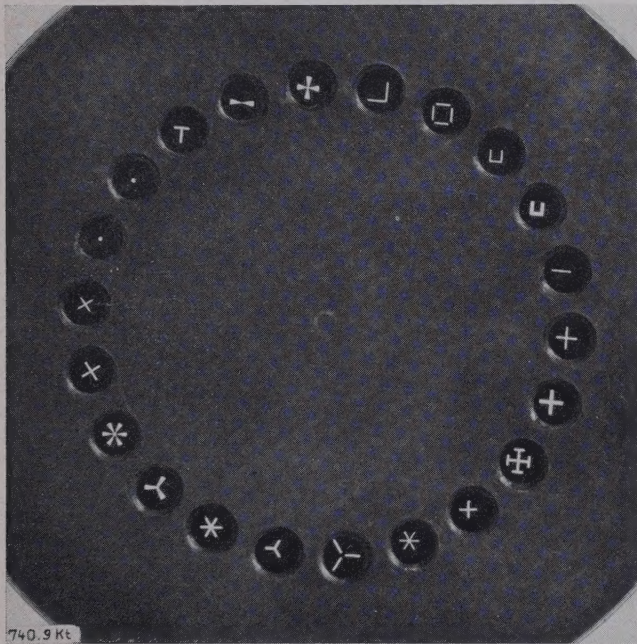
Ausschnitt aus einer Spinddüsenplatte mit im Elektronenstrahlgerät gefrästen Profilen (Edelstahl 0,5 mm dick).
